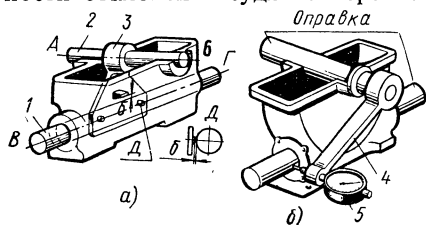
Способы контроля отверстий в корпусе червячной передачи:
